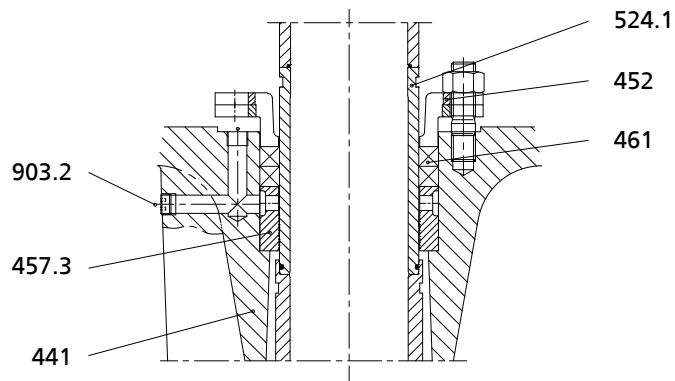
Деталировочный чертеж: Сальниковая набивка
